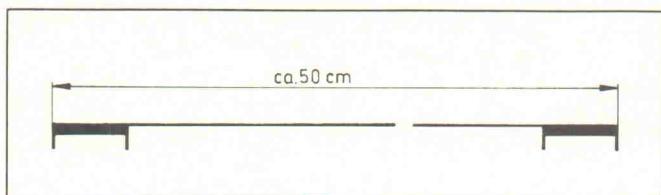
Steckverbinder zwischen CPU und Controllerplatine.
